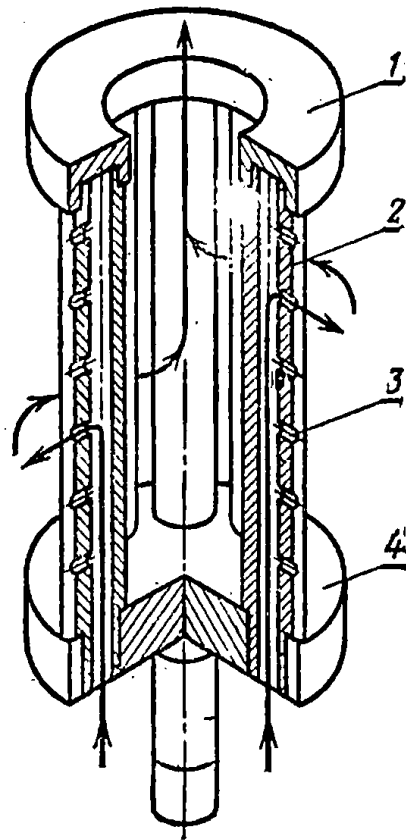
Схема анода для проточного хромирования внутренних поверхностей деталей:
